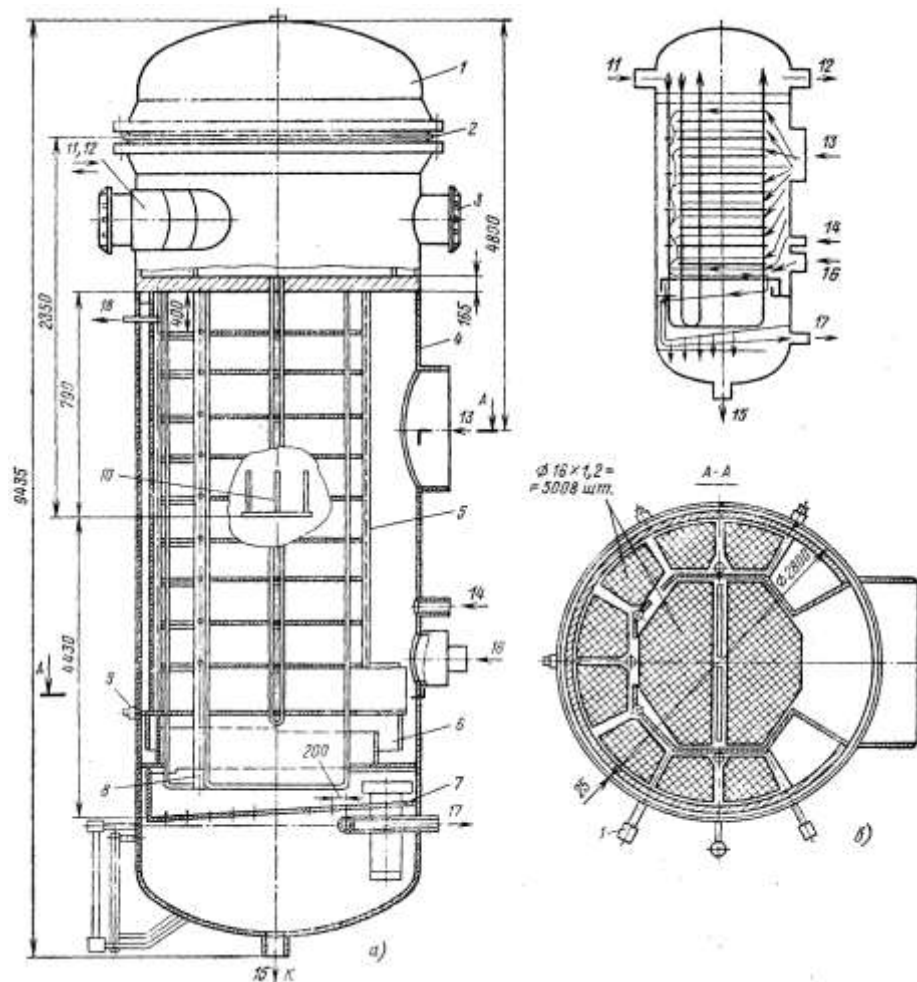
Подогреватель ПН-2300-25-7-У1. Общий вид (а) и схема движения воды и пара (б):
